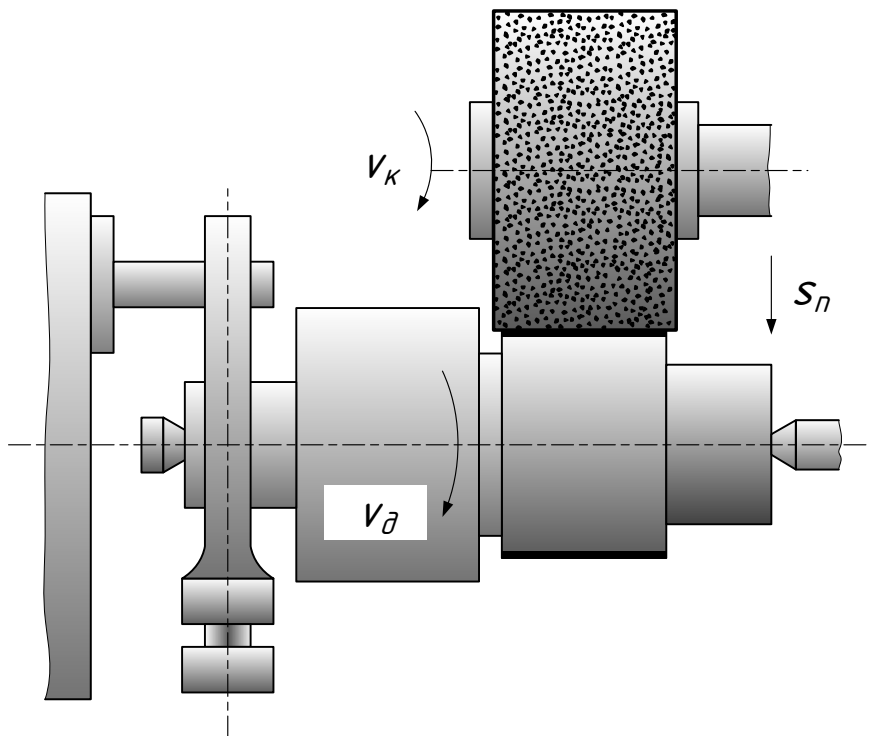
Наружное круглое шлифование врезанием:
